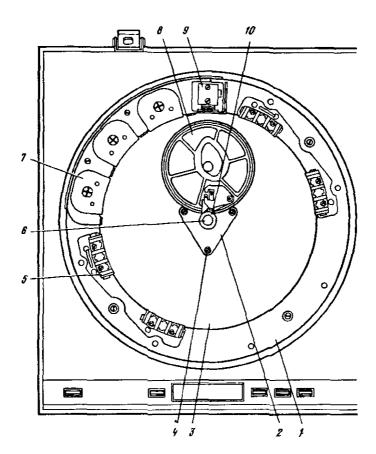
Вид электропроитрывателя со снятым диском: 1 — кольцо; 2 — держатель оси; 3 — цасси; 4 — винт МЗ (3 шт.); 5 — катушка тормоза (4 шт.); 6 — ось; 7 — статорные катушки (3 шт.); 8 — большое зубчатое колесо; 9 — датчик положения ротора; 10 — малое
